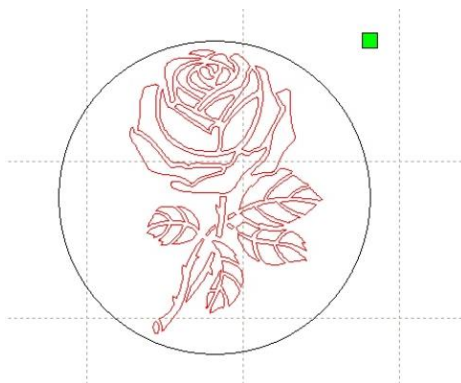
Векторное изображение чертежа детали для гравировки
